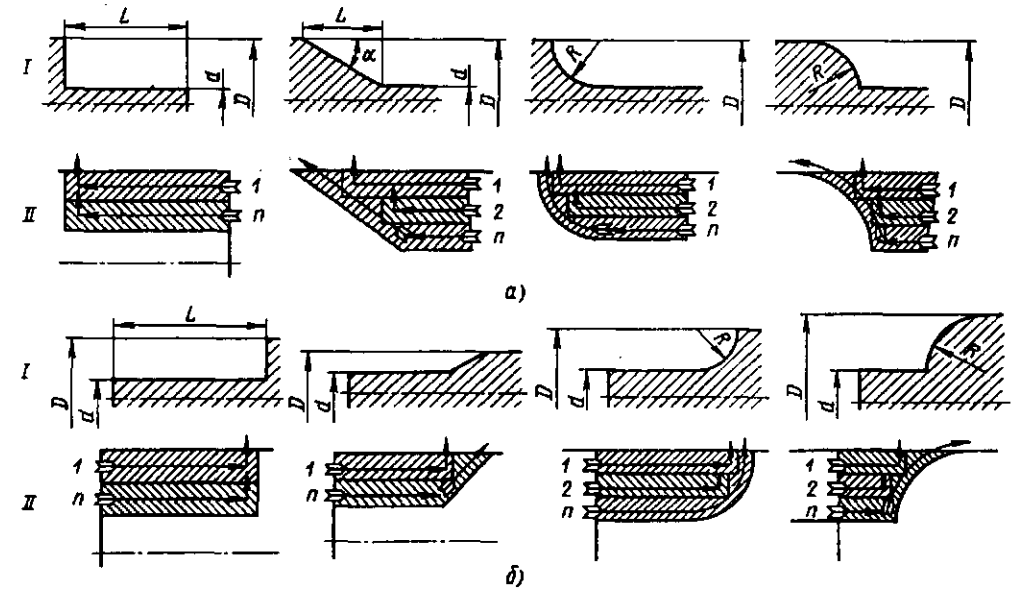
Схемы перемещений проходных резцов при обработке основных участков поверхностей: а – левого резца; б – правого резца; I – эскиз участка поверхности; II – схемы перемещений
